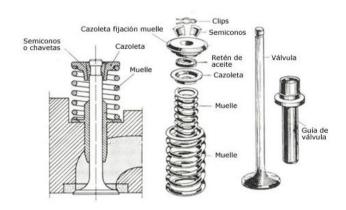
Componentes conjunto de válvula. Fuente. (S.A., Aficionados a la Mecanica, 2012).
